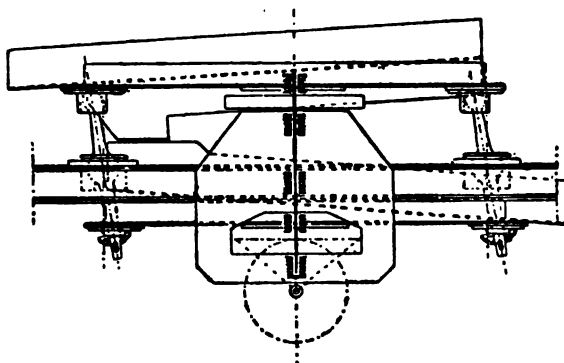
bis. — Crible Schwidtal. — Vue par côté.
